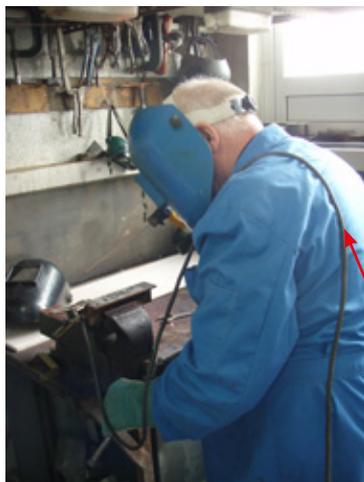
Exemplos de boas e más práticas na passagem do cabo de soldadura por arco
